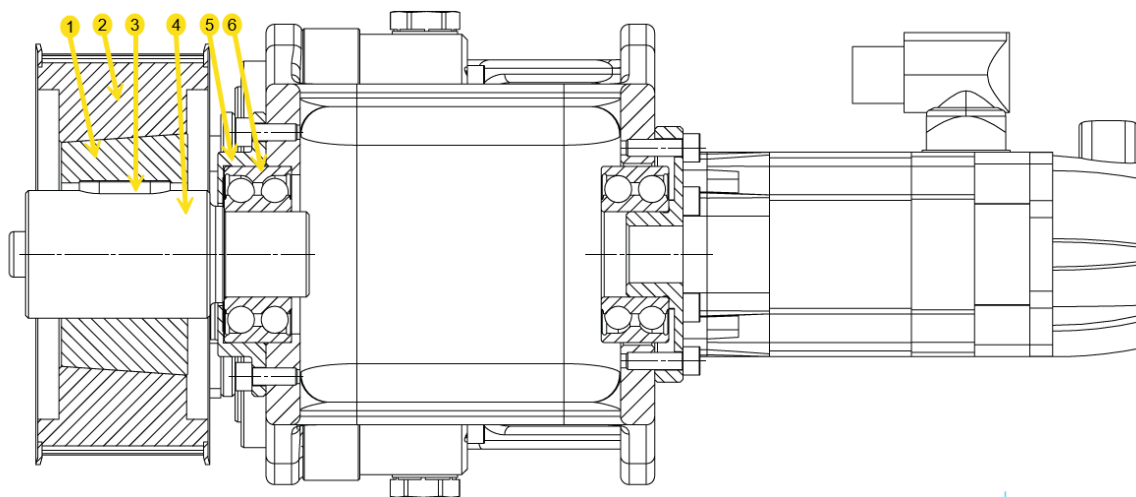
Motor s pastorkem (1-svěrný spoj, 2-lisovaný kroužek, 3-pastorek, 4-motor)
